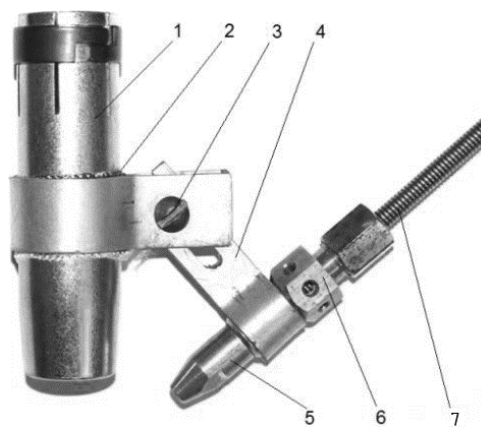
Приспособление для крепления системы ДПП к сварочному автомату АДС-1: 1 – сопло; 2 – токоизолирующий материал; 3 – регулировочный болт; 4 – крепление; 5 – токовый наконечник; 6 – диффузор; 7 – гибкий кабель
